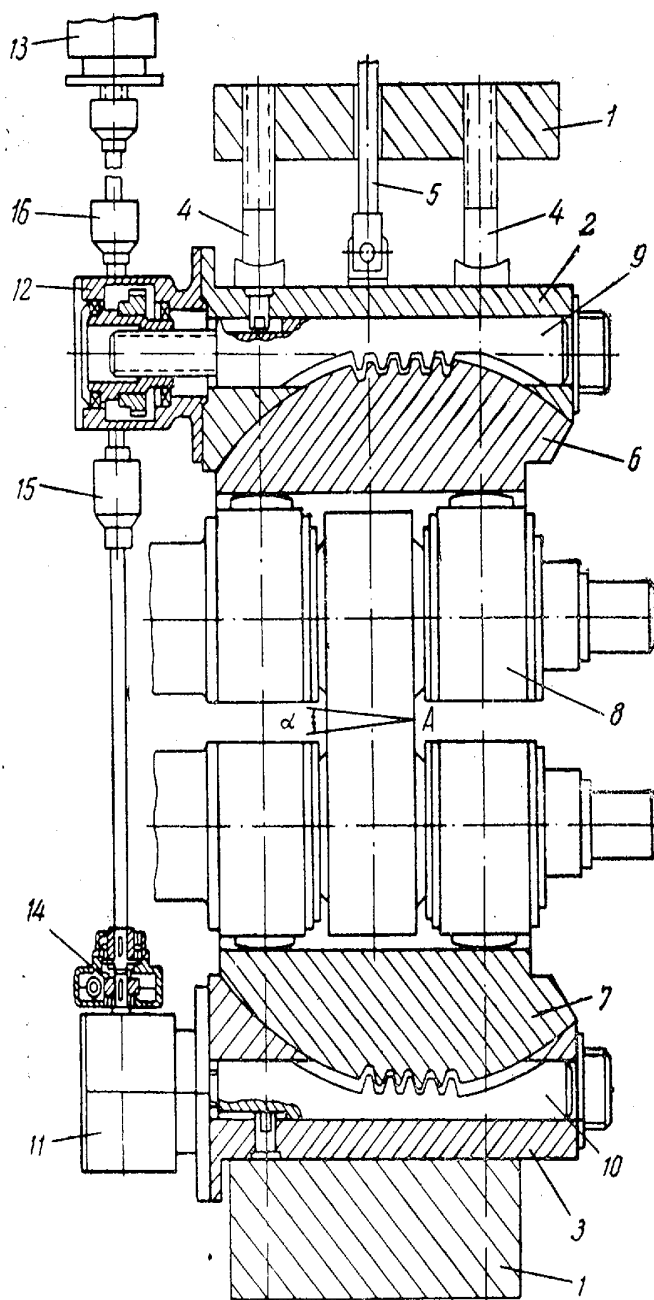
Схема прокатного стана конструкции ВНИИМЕТМАШ для прокатки трапецеидальных полос: 1 – станина; 2 и 3 – кассеты; 4 – нажимные винты; 5 – уравнивающее устройство; 6 и 7 – зубчатые сегменты; 8 – валки; 9 и 10 – зубчатые рейки; 11 и 12 – червячно-цилиндрические редукторы; 13 – электродвигатель; 14 – червячная муфта; 15 и 16 – шпиндели
